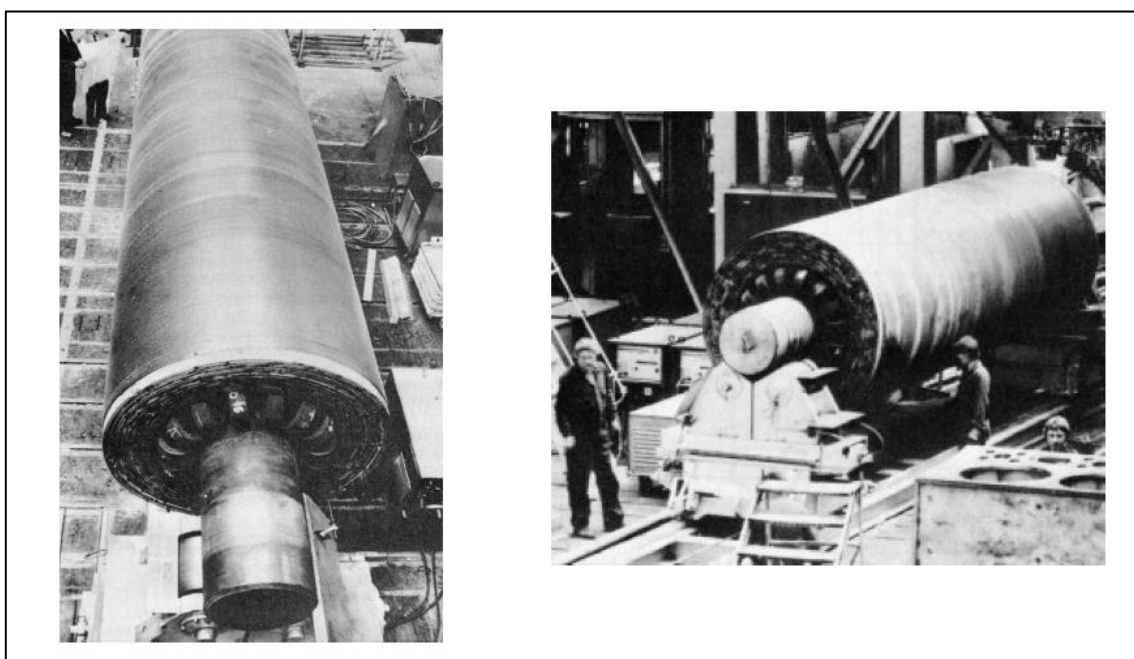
Carcaça de teste cilíndrica de 79 toneladas fabricada por meio soldagem de formas com o processo soldagem arco submerso[5].
